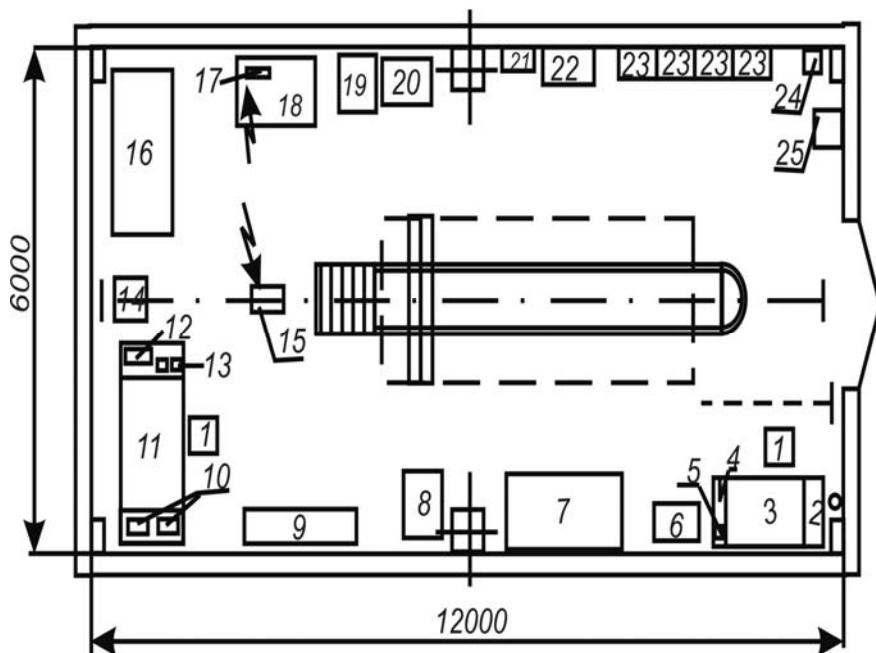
План сварочного участка АТП на 400-500 грузовых автомобилей
